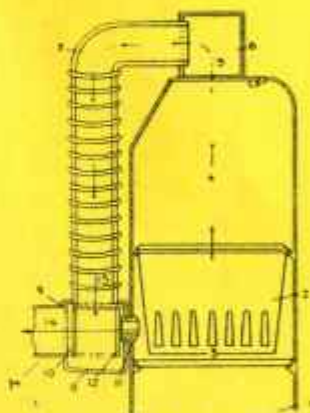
Fig. II. — Elevation latérale montrant la disposition du collecteur récupérateur breveté.
